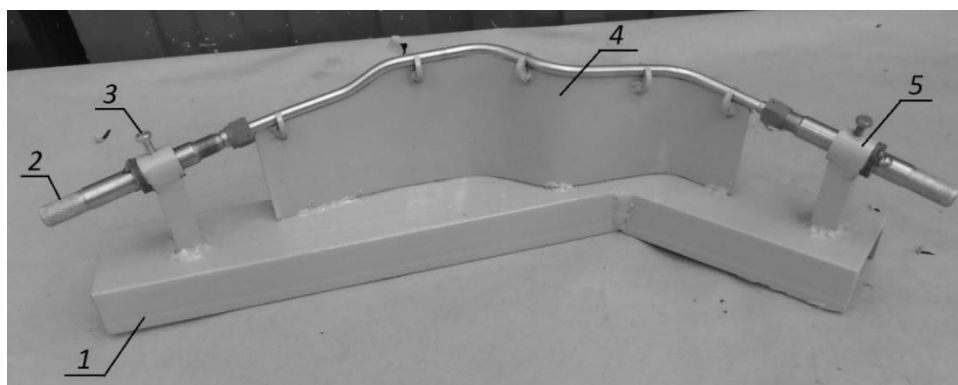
Ступенчатый шаблон для сборки и сварки трубопровода
